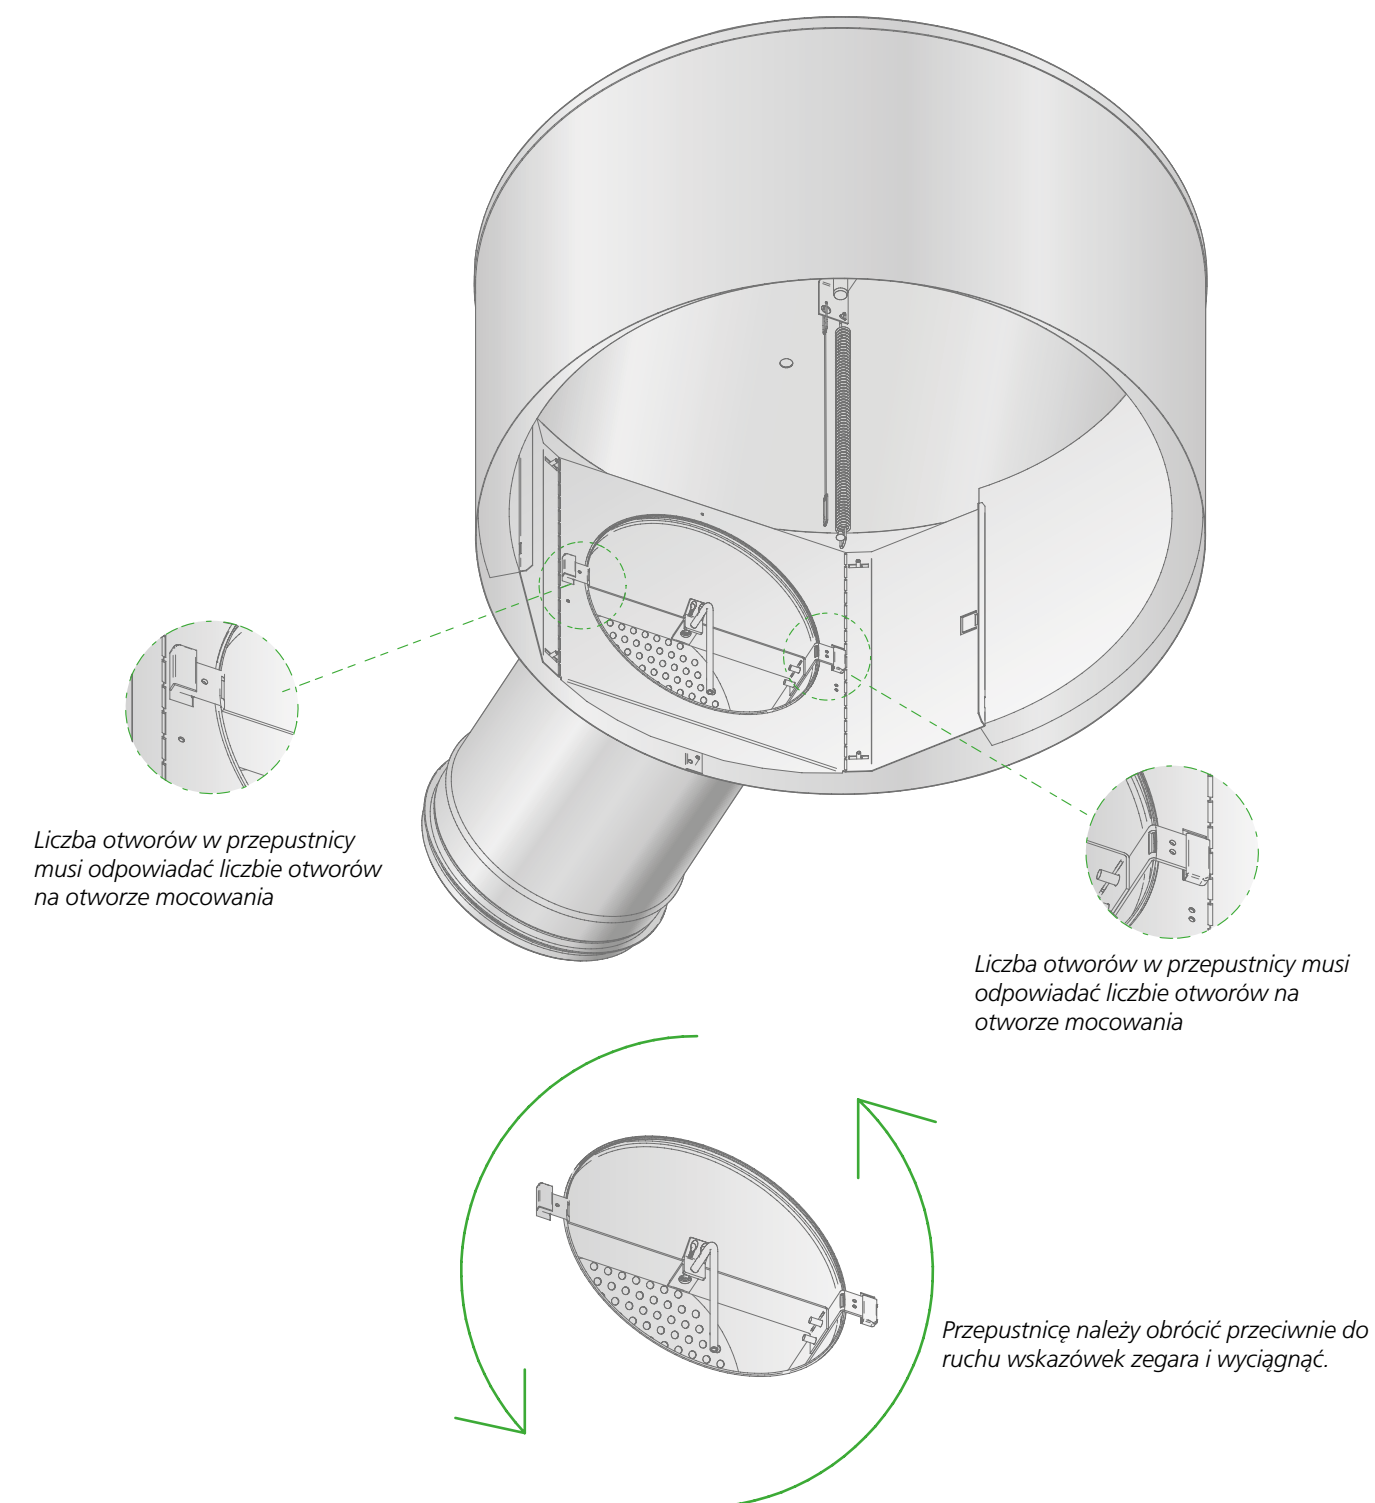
Demontaż płyty stabilizacji strumienia powietrza.
